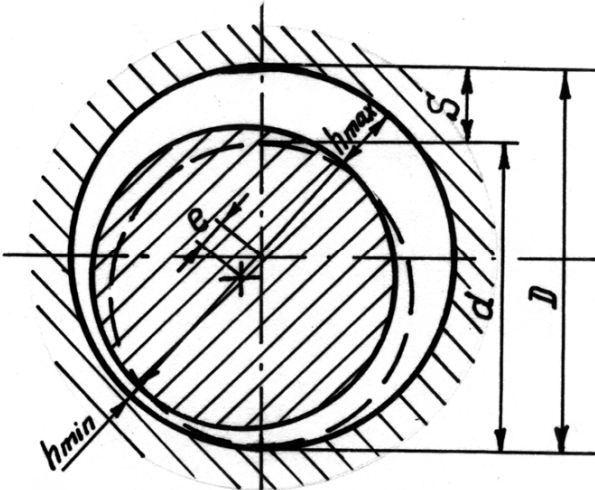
Схема положення вала в з'єднанні підшипник ковзання – вал
